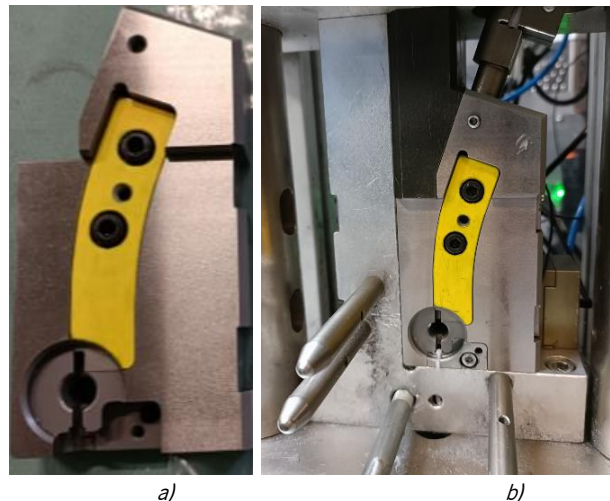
a) Deckel + chapa; b) Máquina de cravação de pinos
